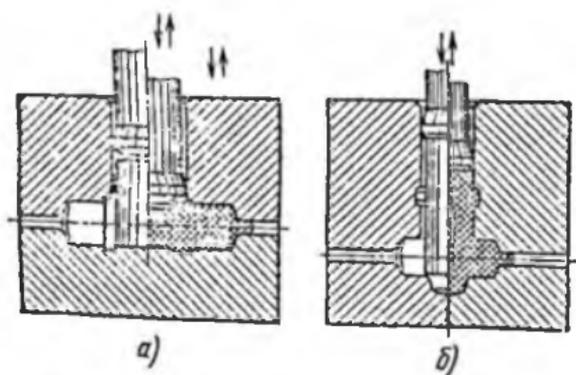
Основные схемы штамповки в разъемных матрицах: а — с горизонтальным разъемом; б — с вертикальным разъемом
